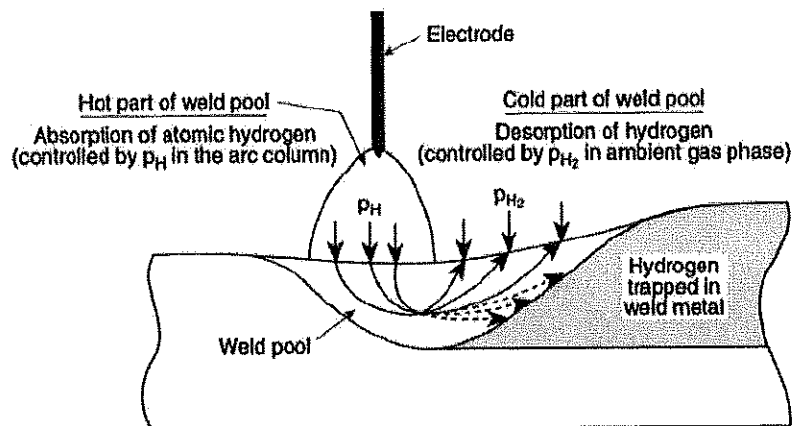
Modelo de reacción idealizado para la captura de hidrógeno en la soldadura de arco, [3-1].
